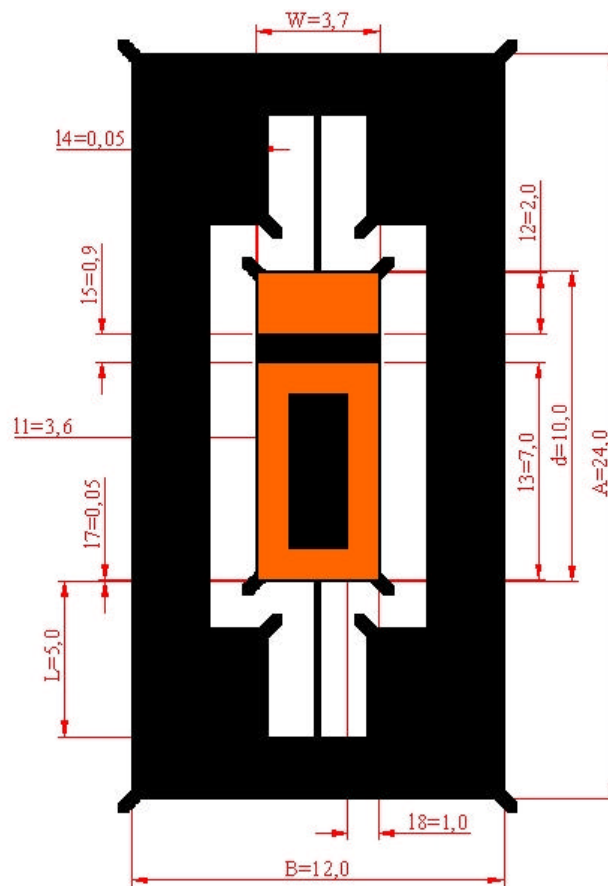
Desenho do Scanner Indutivo e suas dimensões em mm.
